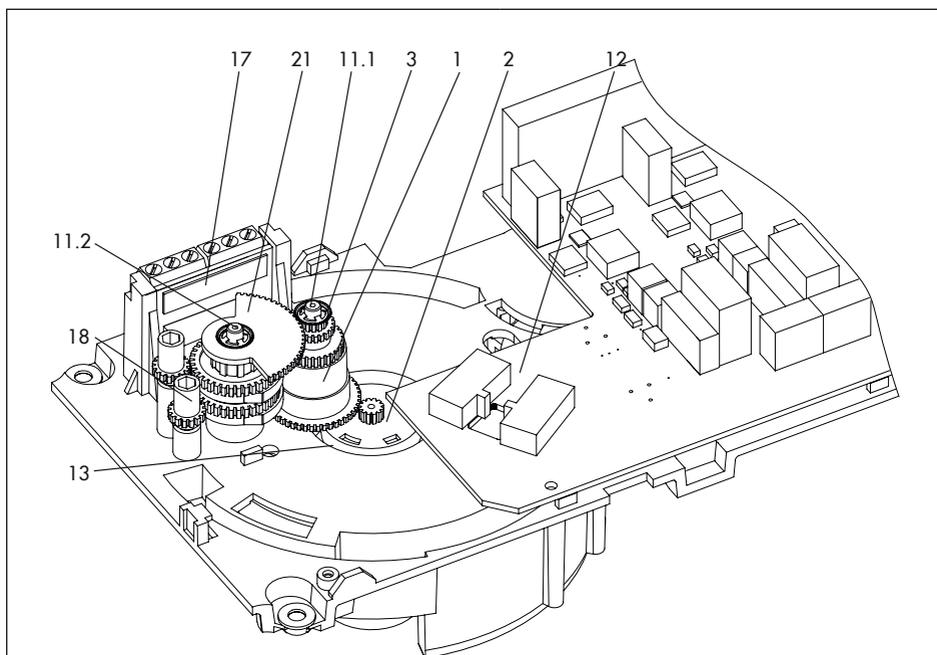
Innenansicht · Antrieb ohne Widerstandsferngeber
